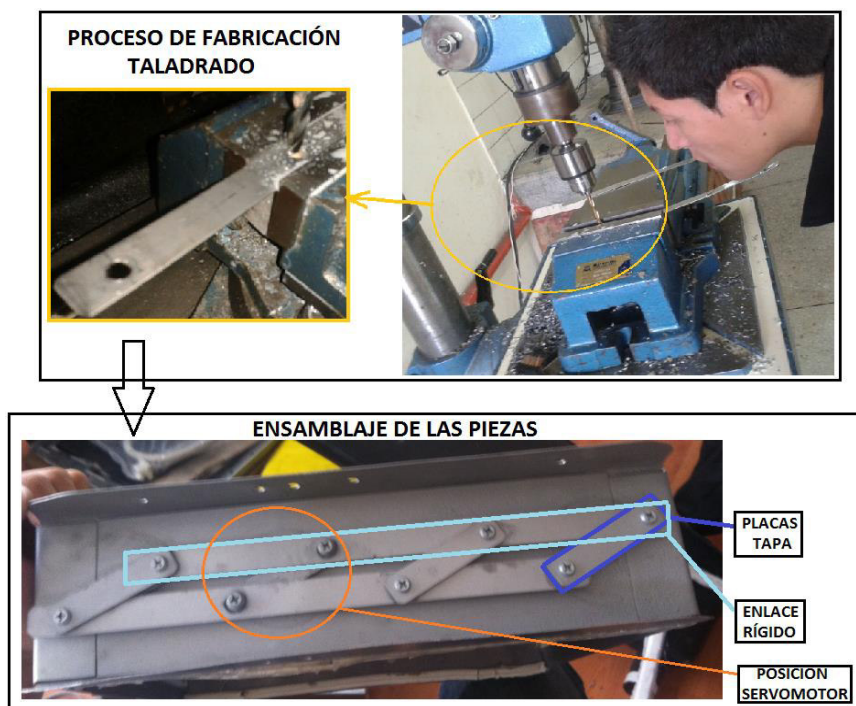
Fabricación de enlace rígido y ensamble en la caja
